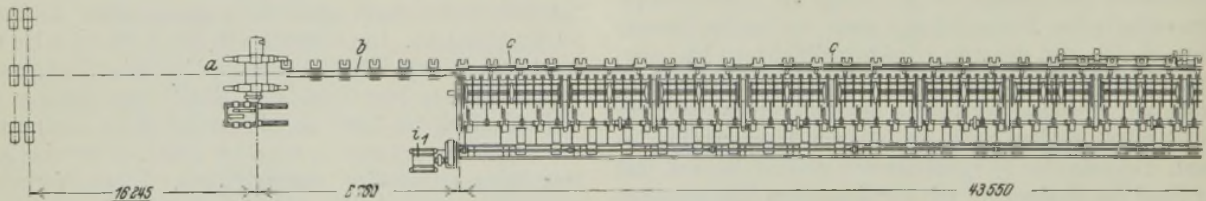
Grundriß des umlaufenden Kühlbettes für ein Edelfeststahlwerk.
